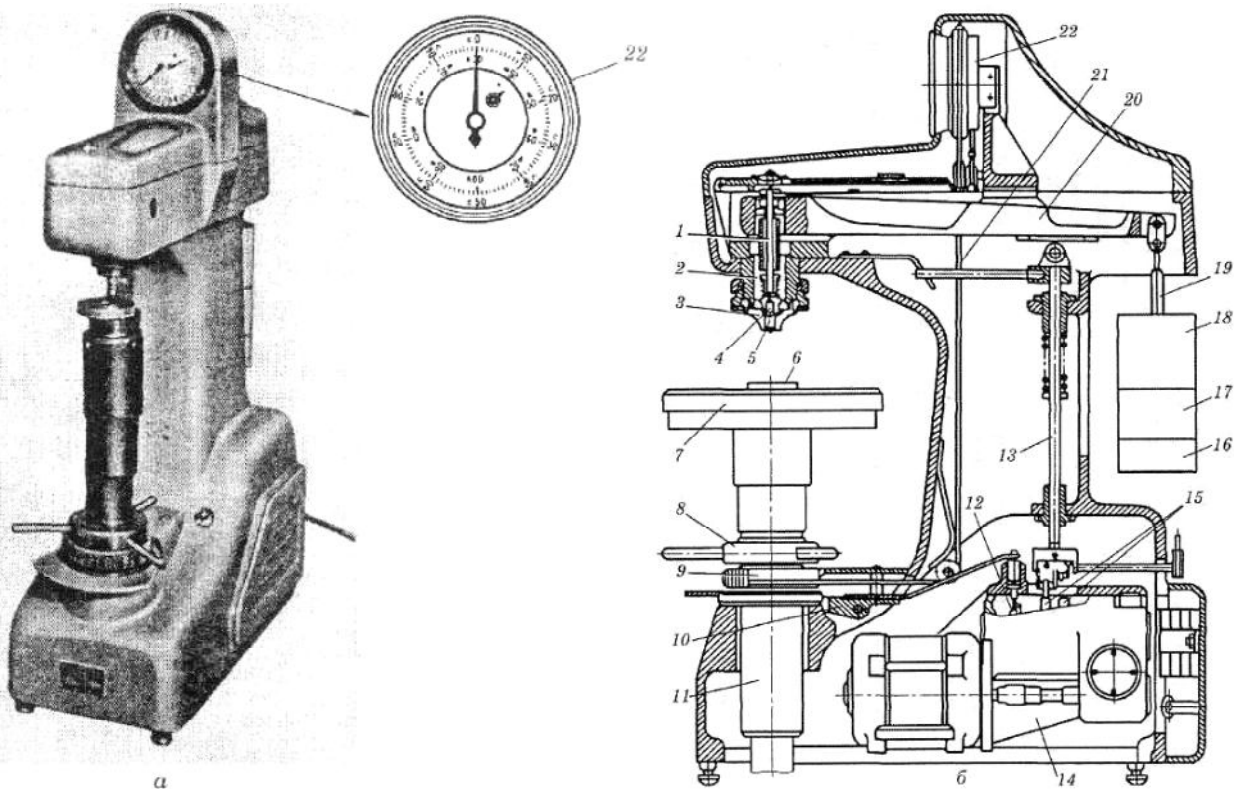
а – загальний вигляд твердоміра Роквелла; б – кінематична схема
